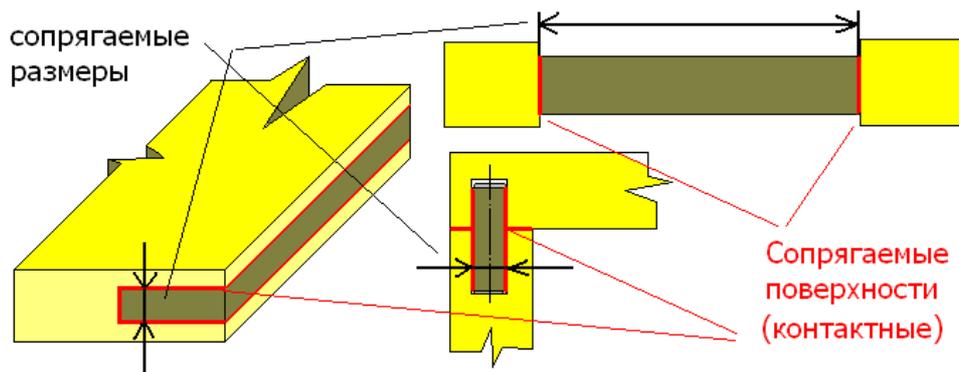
Сопрягаемые, контактные поверхности в соединении деталей
